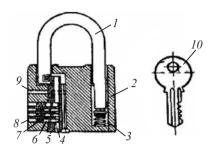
Схема навесного цилиндрового штифтового замка: I – дужка; 2 – корпус; 3 – пружина дужки; 4, 6 – штифты; 5 – цилиндр; 7 – пружина штифта; 8 – заглушка; 9 – упорный штифт цилиндра; 10 – ключ
